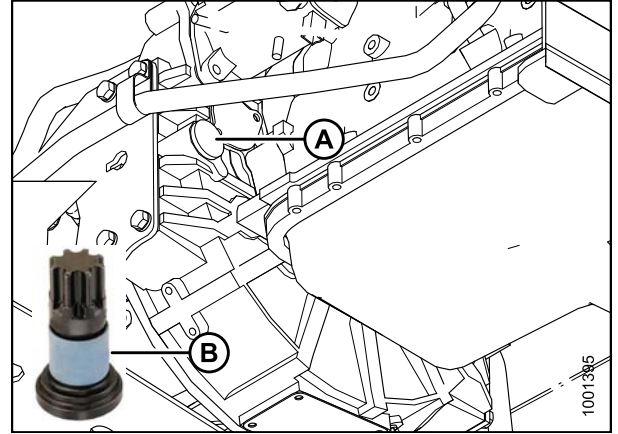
Расположение отверстия для работы с инструментом для проворачивания коленвала
